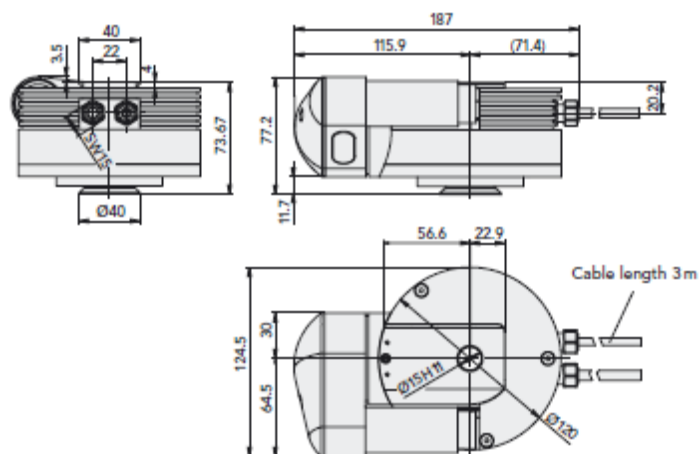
Вращательный модуль DAE-60 : габаритный чертеж и внешний вид
